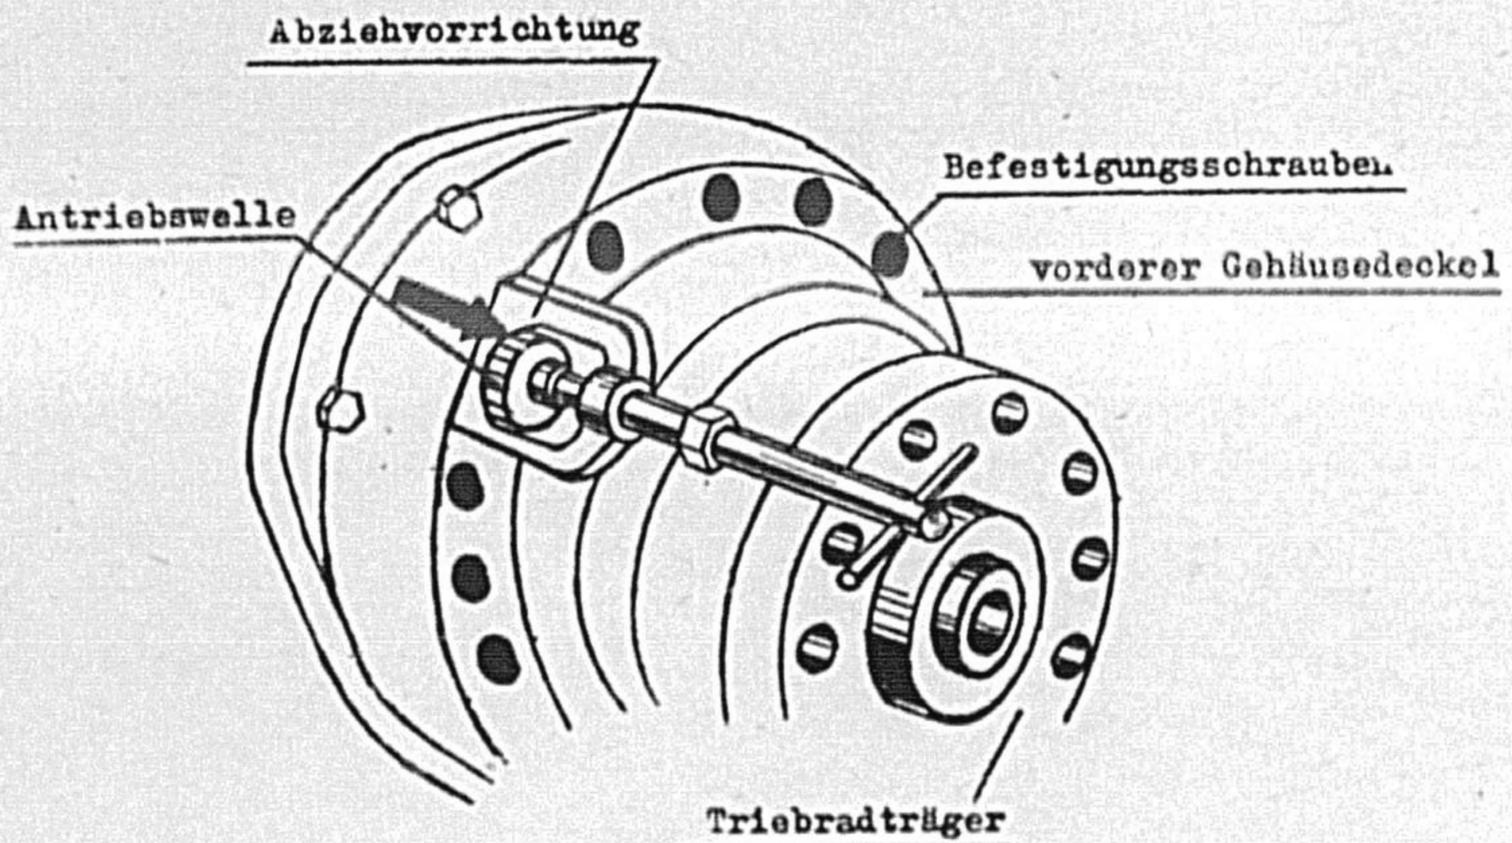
Ausziehen der Antriebswelle und Lösen der Befestigungsschrauben
